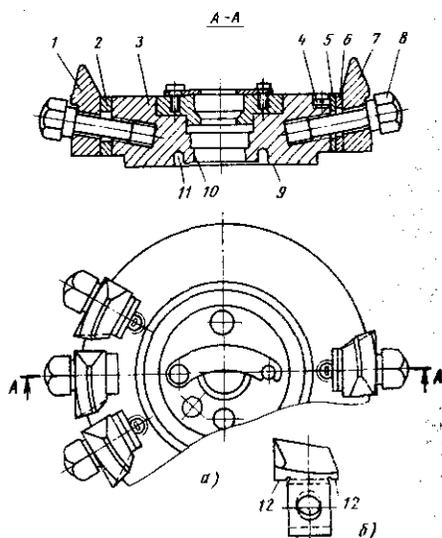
Чистовая режущая головка типа Хардак: а — общий вид головки; б — резец
